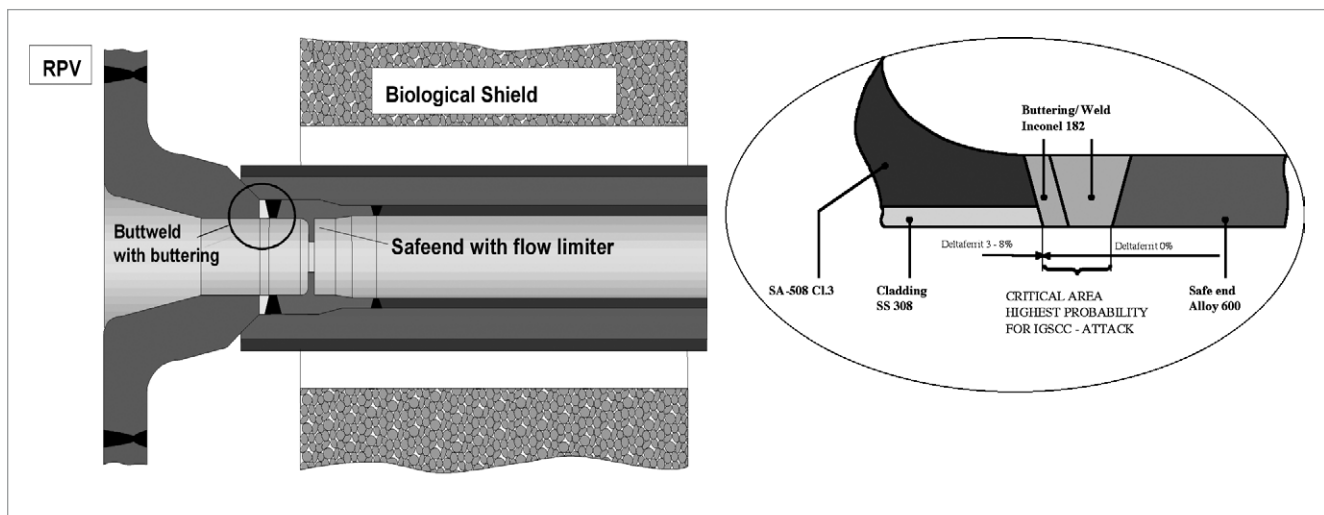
Soldaduras unión aceros distint. típicas de recipiente presión reactor BWR.
